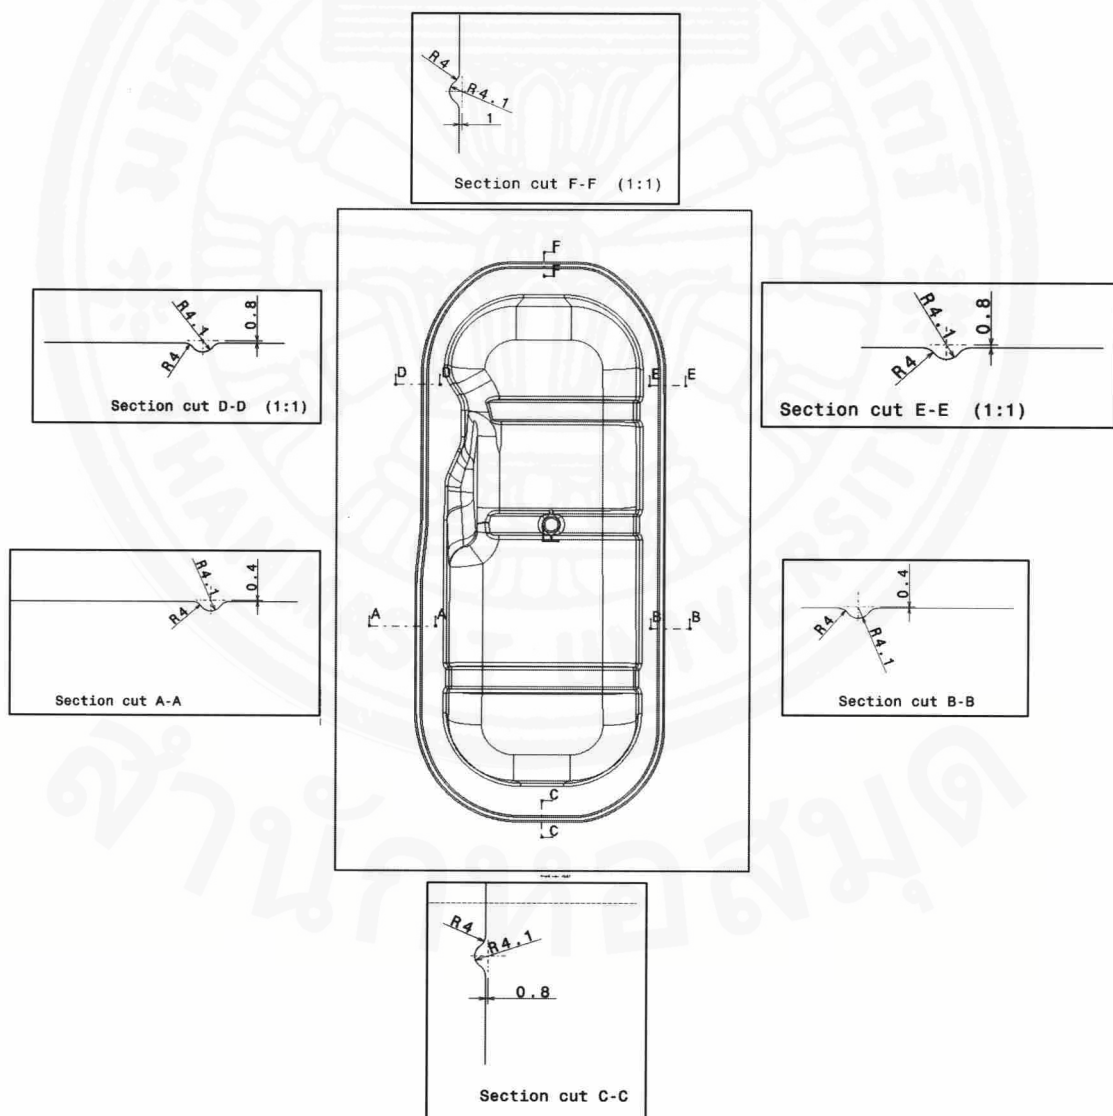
แสดงภาพ Tooling พร้อม Drawbead
